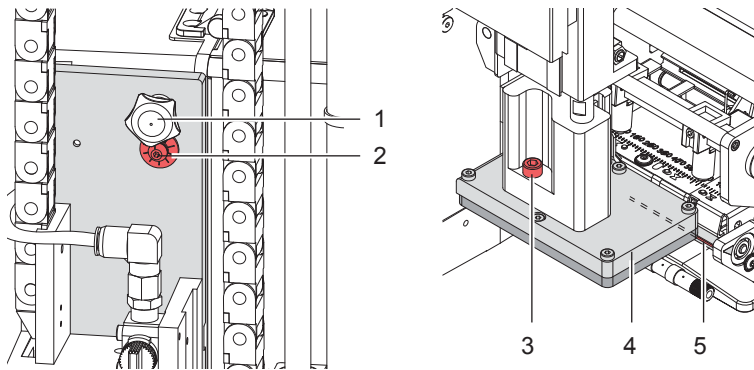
Positionnement de la semelle par rapport à l'arête de pré-décollement
